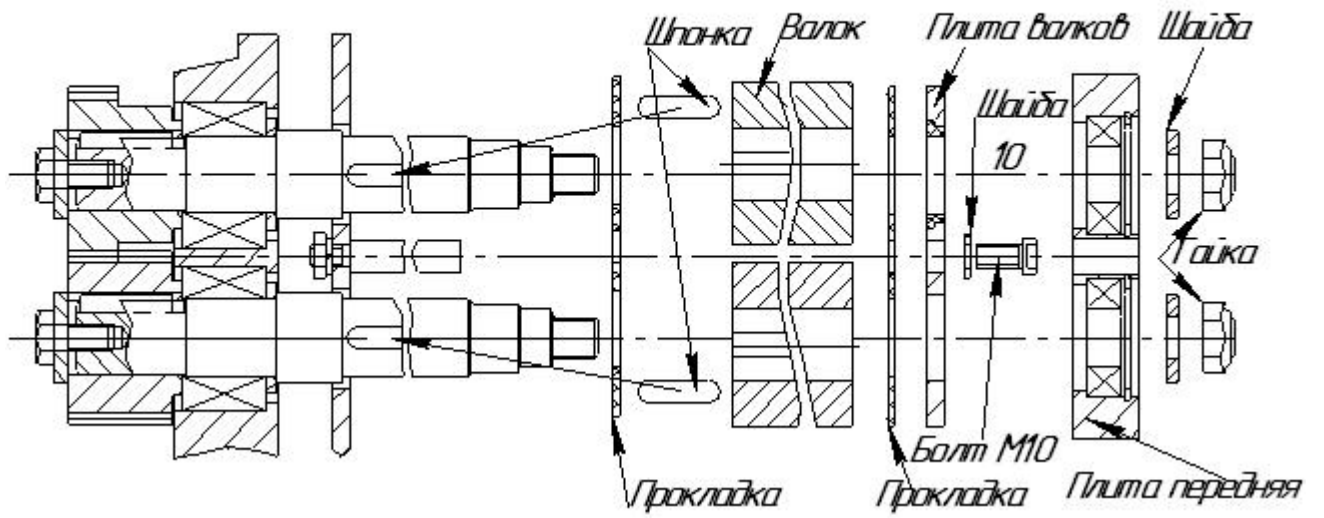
Чертеж - порядок сборки (разборки) узла раскатки.
